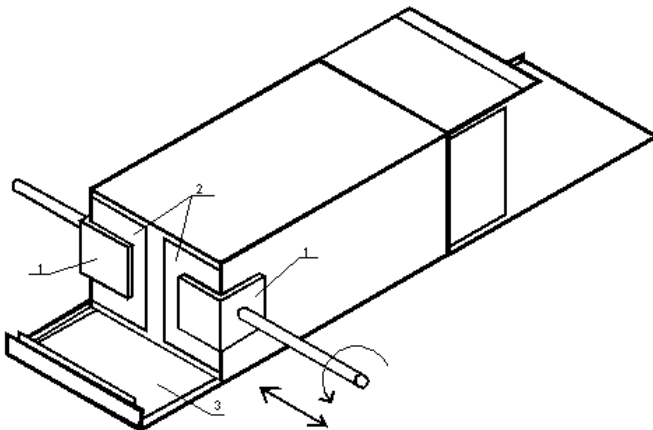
Схема формування картонної пачки: 1 – маніпулятори; 2 – бокові клапани; 3 – задній клапан
